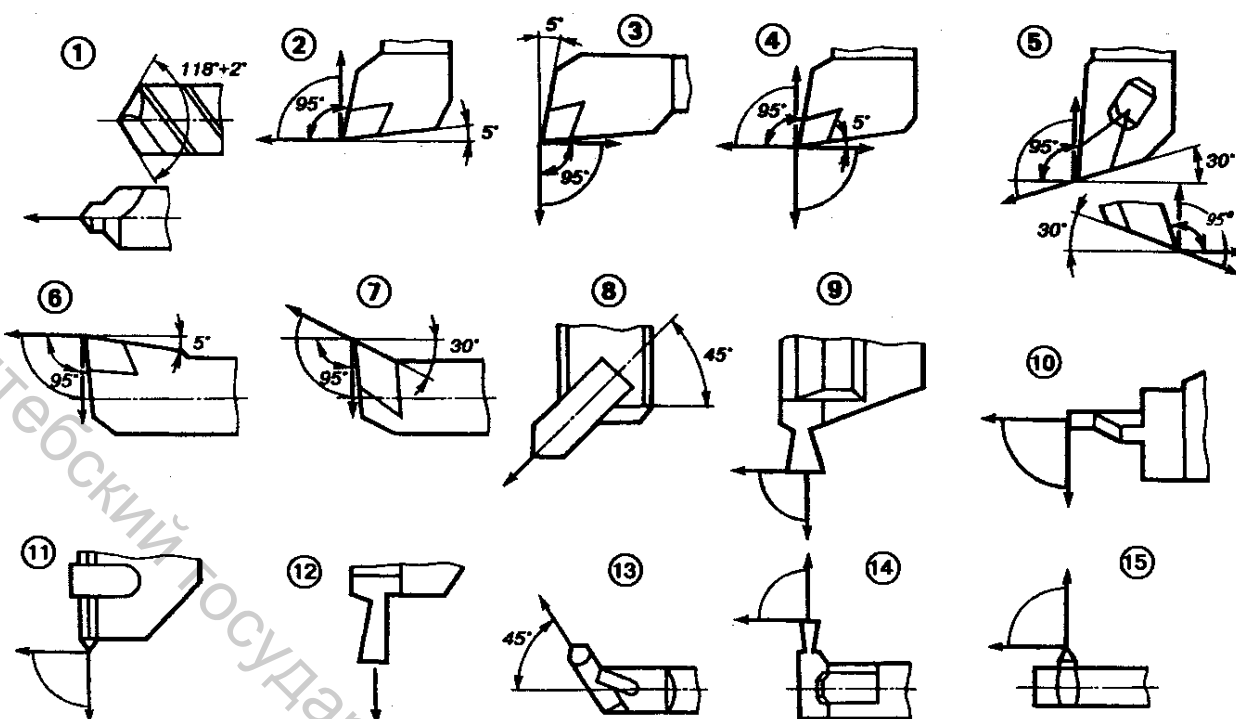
Номенклатура режущего инструмента для токарных станков с ЧПУ с указанием зон направления рабочей подачи:
